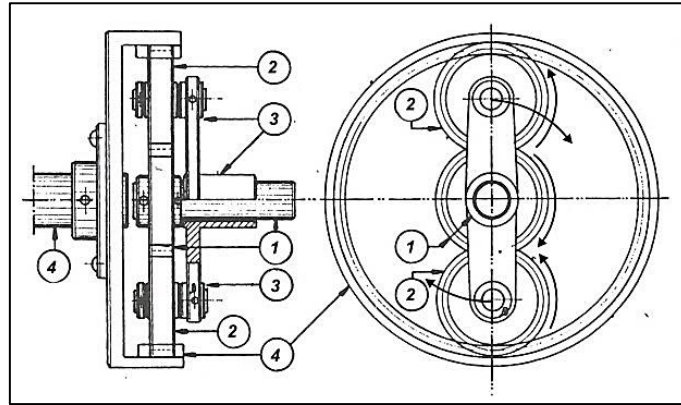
Ejemplo transmisión por engranajes epicicloidal.
